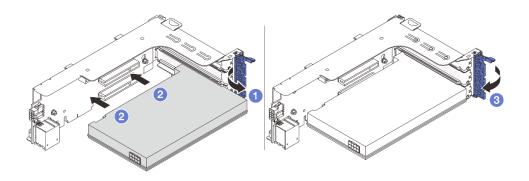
Установка адаптера PCIe в блок платы-адаптера Riser 1 или 2
